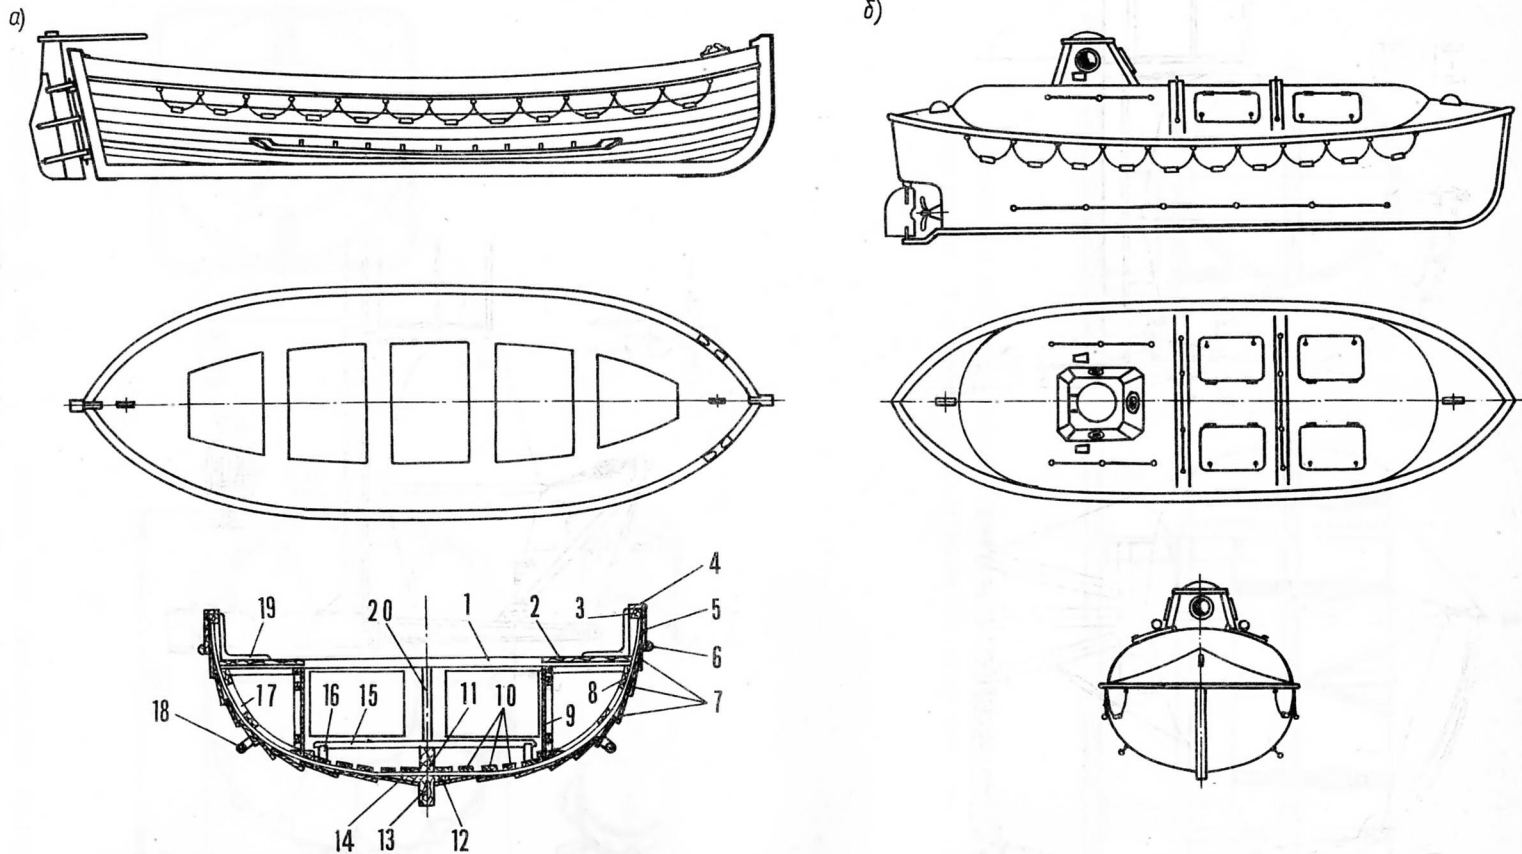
Конструкция спасательной шлюпки; а — деревянной класса 1А; б — пластмассовой закрытого типа
